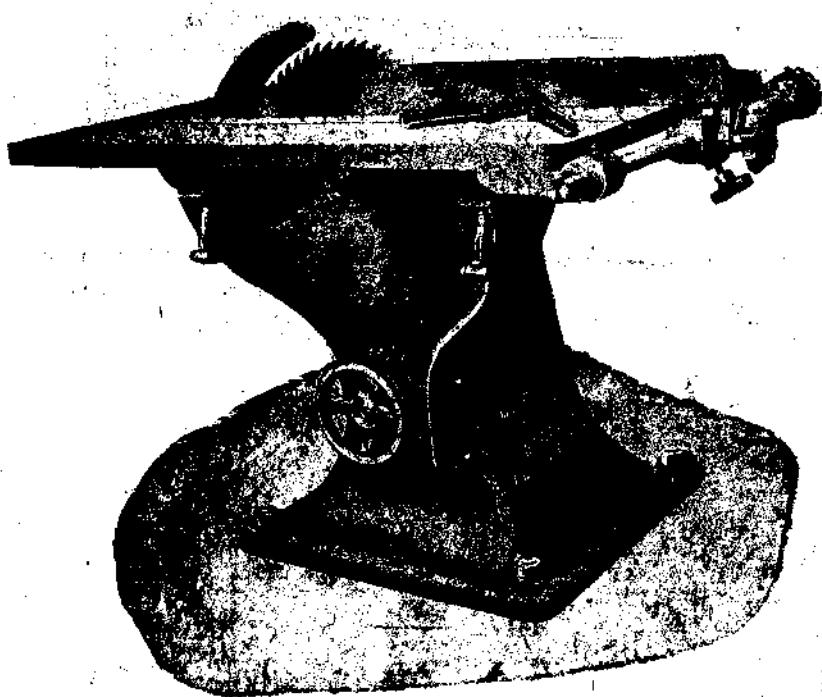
Универсальный станок с круглой пилой для столярных работ.
